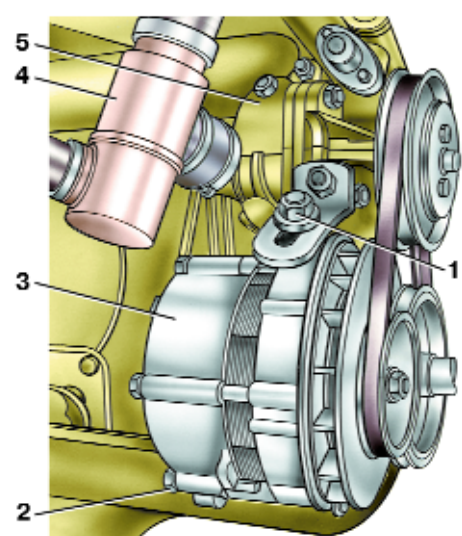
Привод генератора и жидкостного насоса двигателя мод. 2106-70: 1 - гайка крепления генератора к регулировочной планке; 2 - гайка пальца шарнирного крепления генератора; 3 - генератор; 4 - термостат; 5 - жидкостный насос
